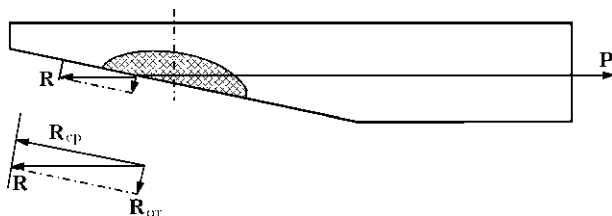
Схема равновесия одной из деталей предлагаемого сварного соединения
